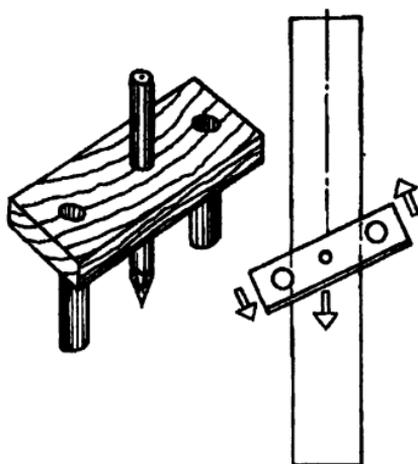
Приспособление для проведения осевой линии на заготовке
